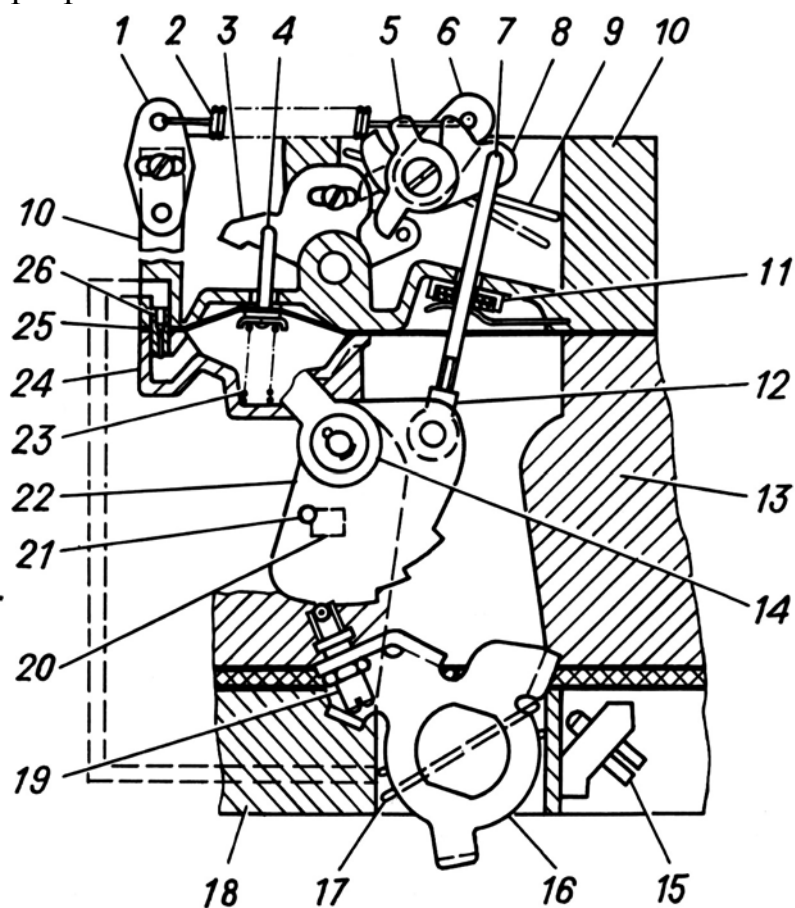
Схема полуавтоматического устройства пуска и прогрева: 1, 5, 6 и 16 - рычаги; 2 - пусковая пружина; 3 - промежуточный рычаг; 4 - тяга пневмокорректора; 7 - тяга; 8 - секторный рычаг; 9 - воздушная желонка; 10 - крышка карбюратора; 11 - уплотнительный элемент; 12 - регулировочная муфта; 13 - корпус поплавковой камеры; 14 - рычаг привода воздушной заслонки; 15 - упорный винт дроссельной заслонки первичной секции карбюратора; 17 - дроссельная заслонка первичной секции карбюратора; 18 - корпус смесительных камер; 19 - винт с роликом; 20 - упор; 21 - штифт; 22 - профильный рычаг; 23 - пружина пневмокорректора; 24 - крышка пневмокорректора; 25 - диафрагма; 26 - жиклер пневмокорректора
